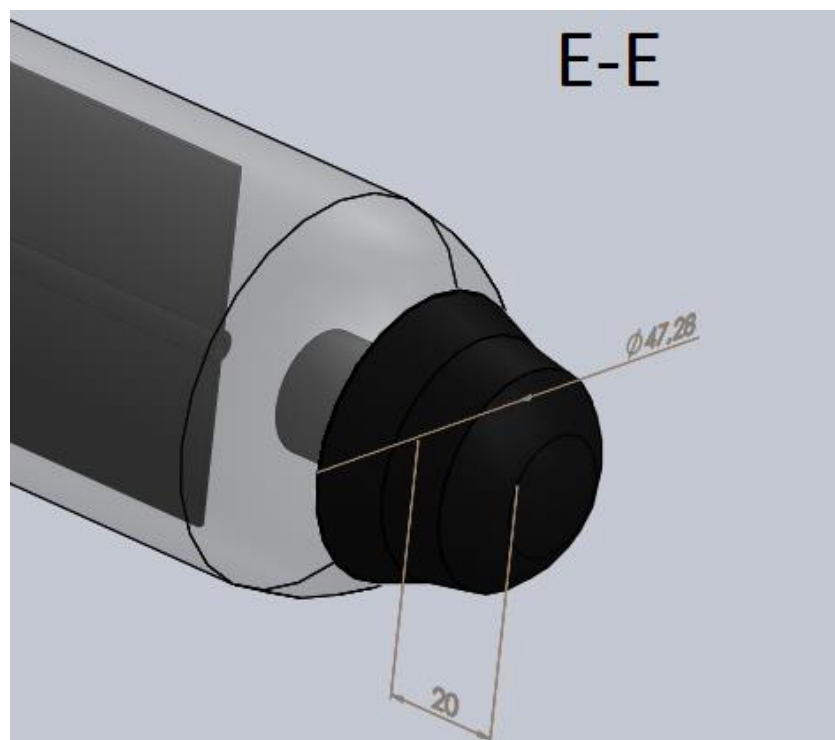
Desenho tridimensional do detalhe E-E do tubo de vácuo.
